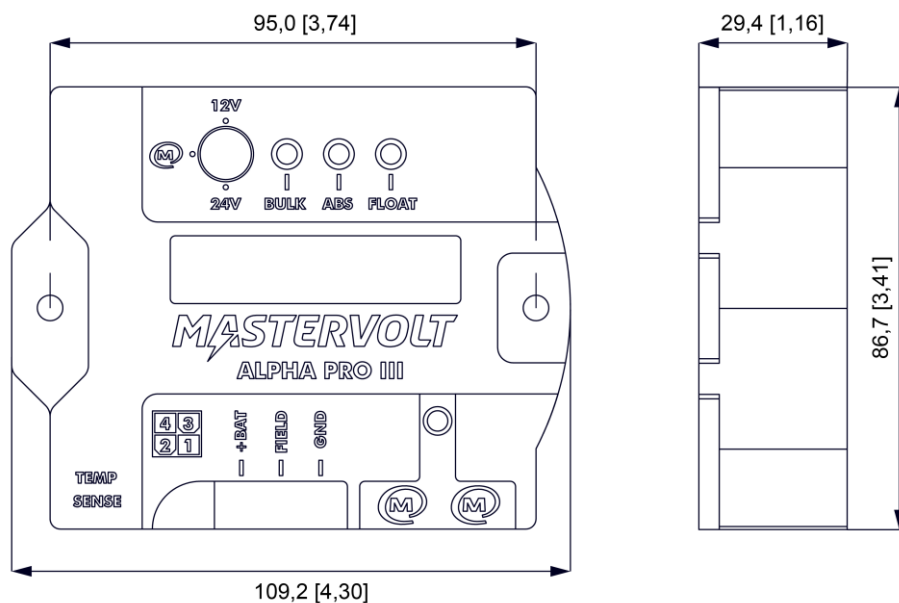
Maßzeichnungen Alpha-Pro-Regler in mm [Zoll]
